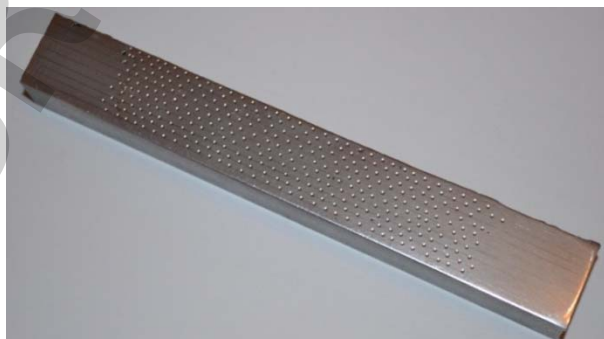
Заготовка після вимірювань твердості на приладі ТР-5006 (Росія)
